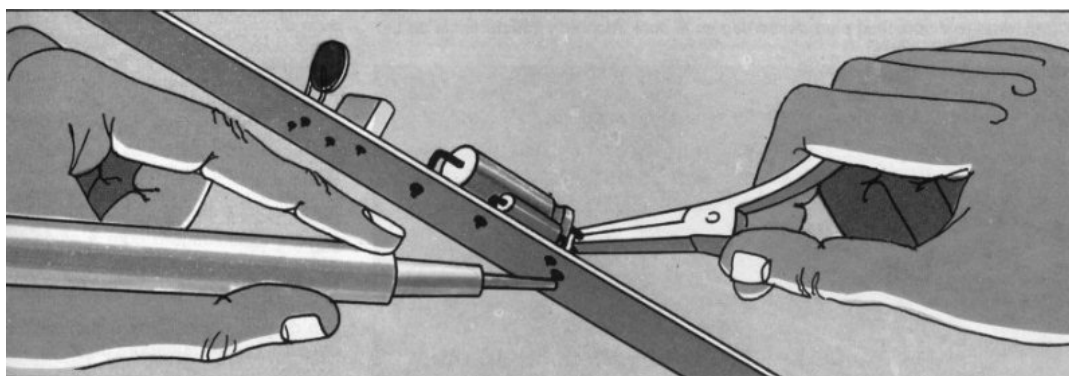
A dessoldagem por aplicação de soldador e tração simultânea pode danificar o componente ou o circuito (extraído de [1]).
